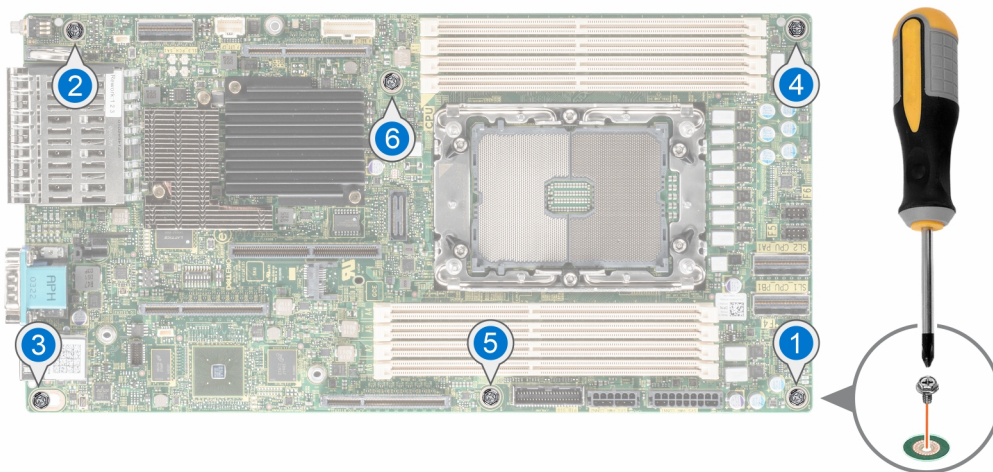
Reihenfolge bei der Befestigung der Schrauben auf der Hauptplatte
